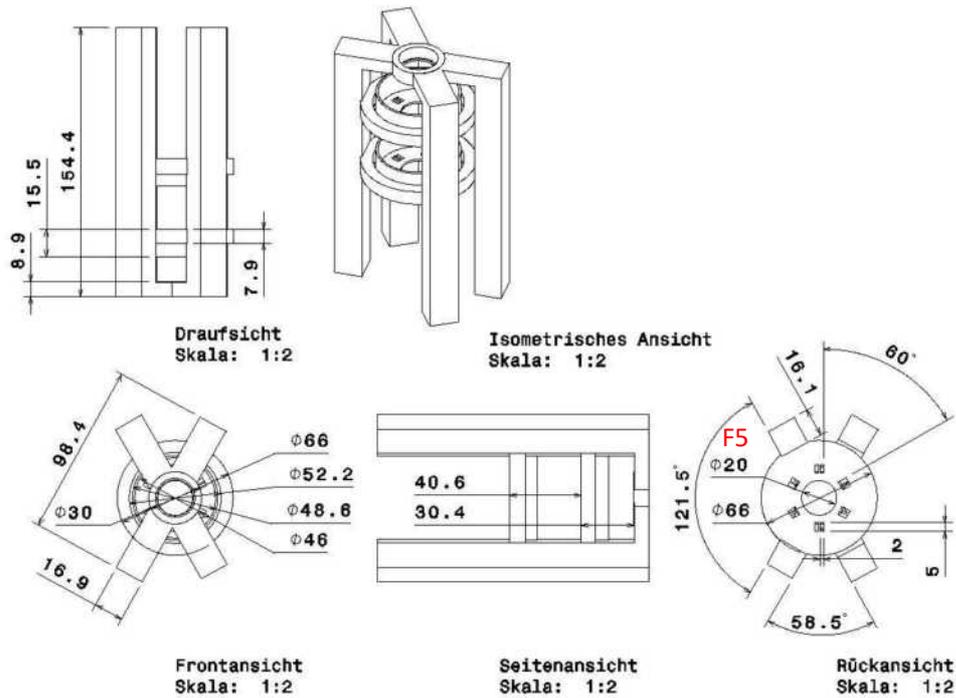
Element 3 (2D-Zeichnung) mit Toleranz
